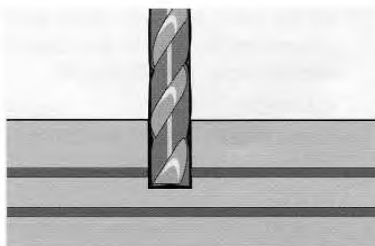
а – Фрезерование печатной платы по точным координатам
